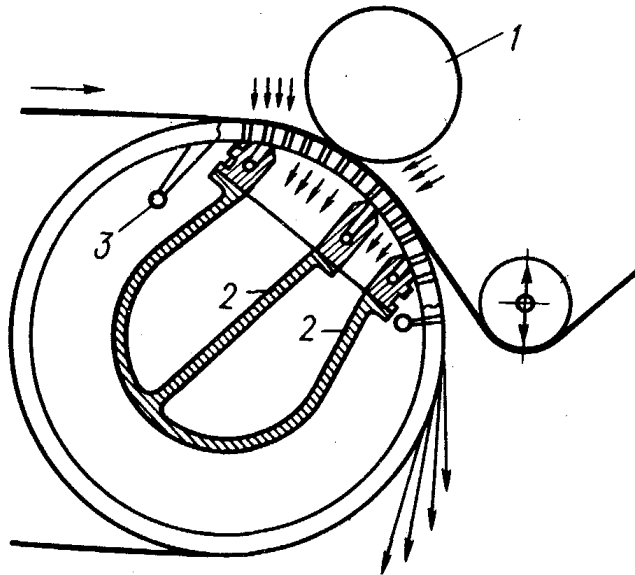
Схема двохкамерного гауч-вала: 1 – притискний валик; 2 – вакуумна камера; 3 – збризкування.
